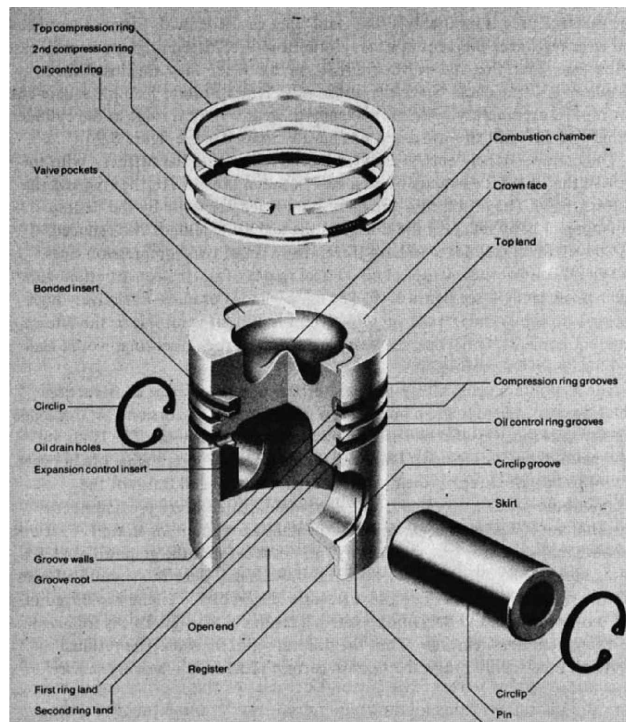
Ensamblaje de anillos en un pistón GKN Engine Parts Division [3]
